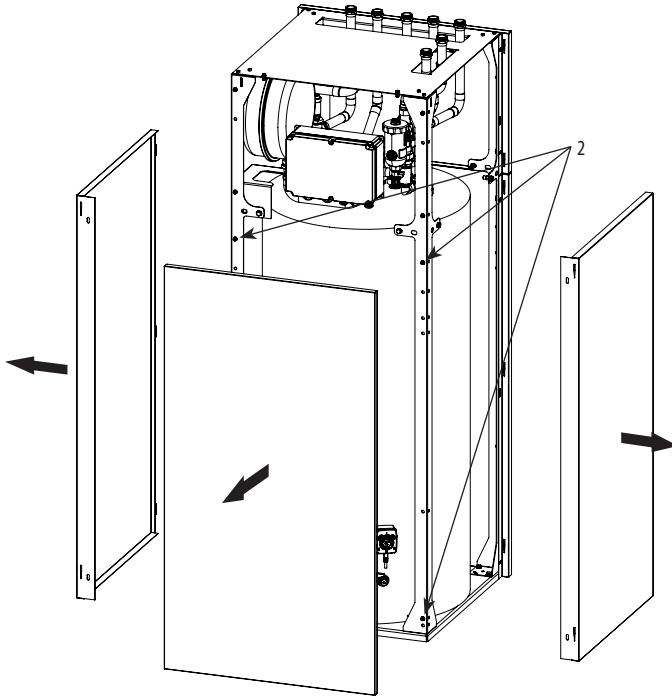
Onebox - Demontage der unteren Gehäusewände
